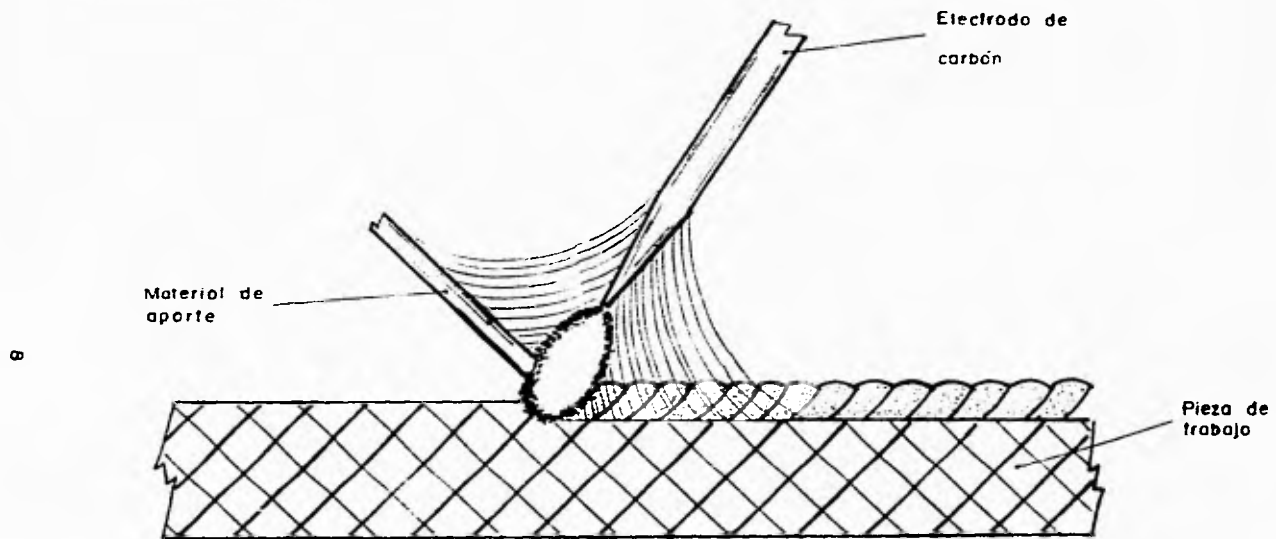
Soldadura por arco de carbón (CAW)
